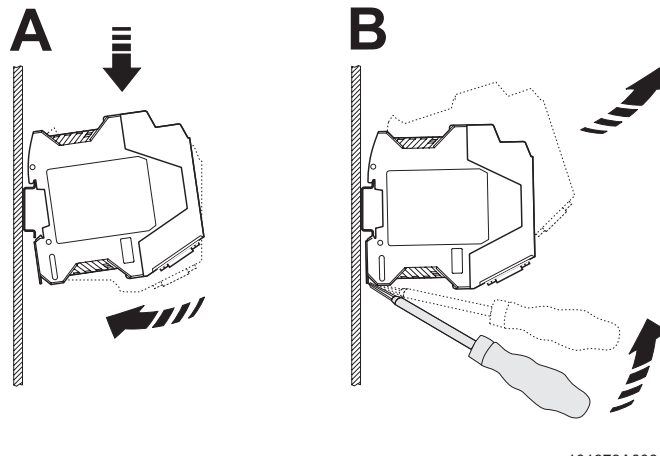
Montaggio e smontaggio di un dispositivo singolo
